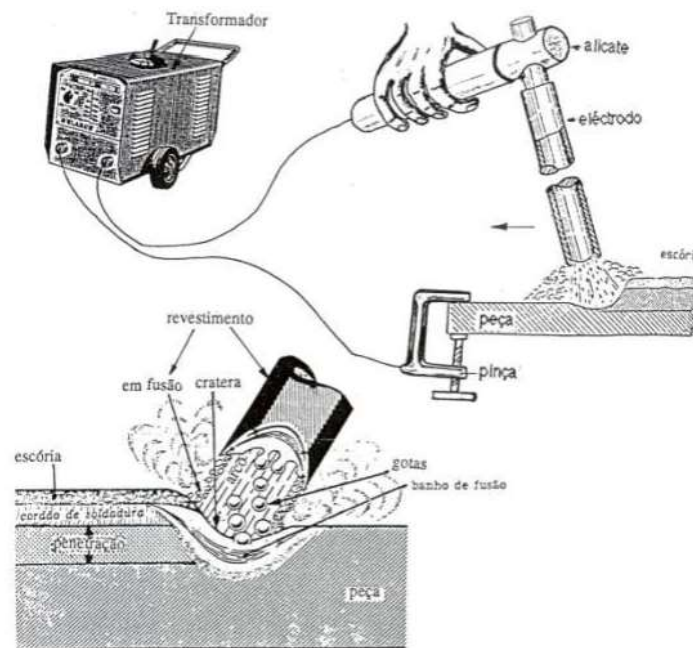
Ilustração esquemática do processo de soldadura SER. [1]
